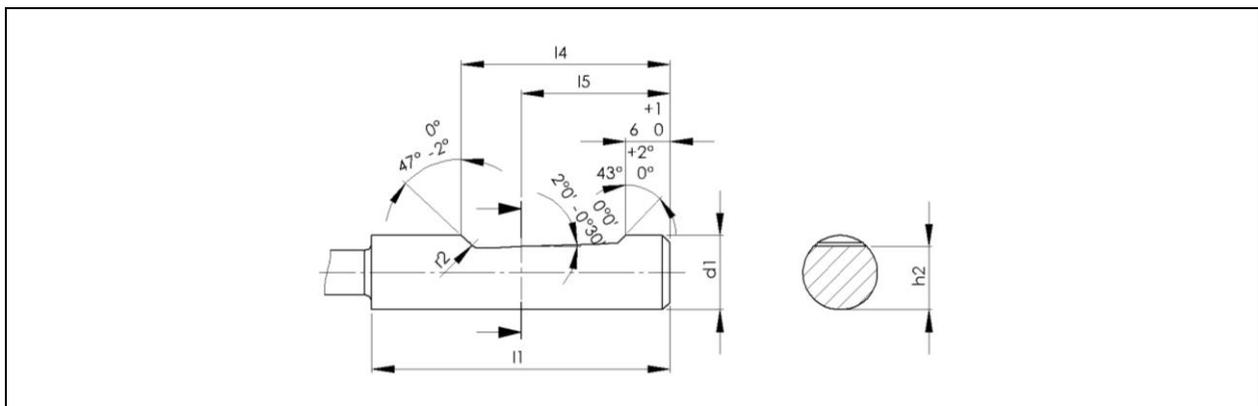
Abmessungen bei Werkzeugen mit Zylinderschaft mit geneigter Mitnahmefläche
